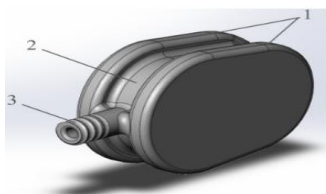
Схема внеротового блока. 1 – щечный и язычный щит; 2 – корпус устройства; 3 – штуцер для соединения с воздушной магистралью.
